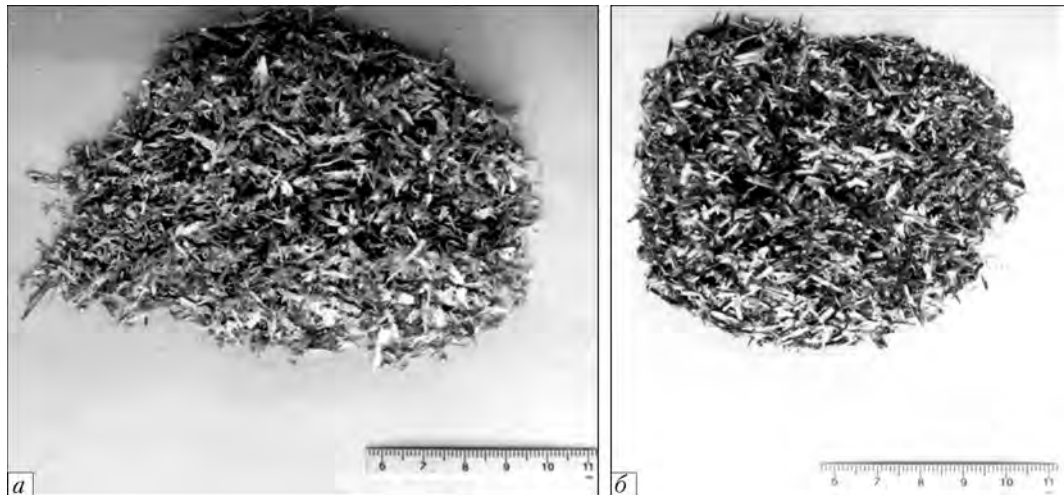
Быстрозакаленный чешуйчатый материал: *а* – алюминиевый сплав Д16; *б* – титан ВТ1-0
